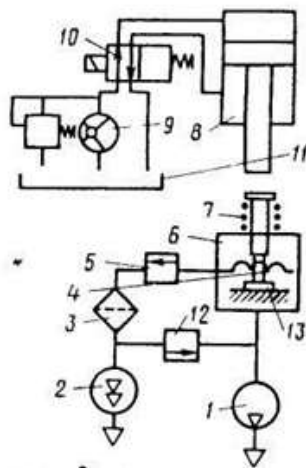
Схема установки для диффузионной сварки с индукционным нагревом деталей
